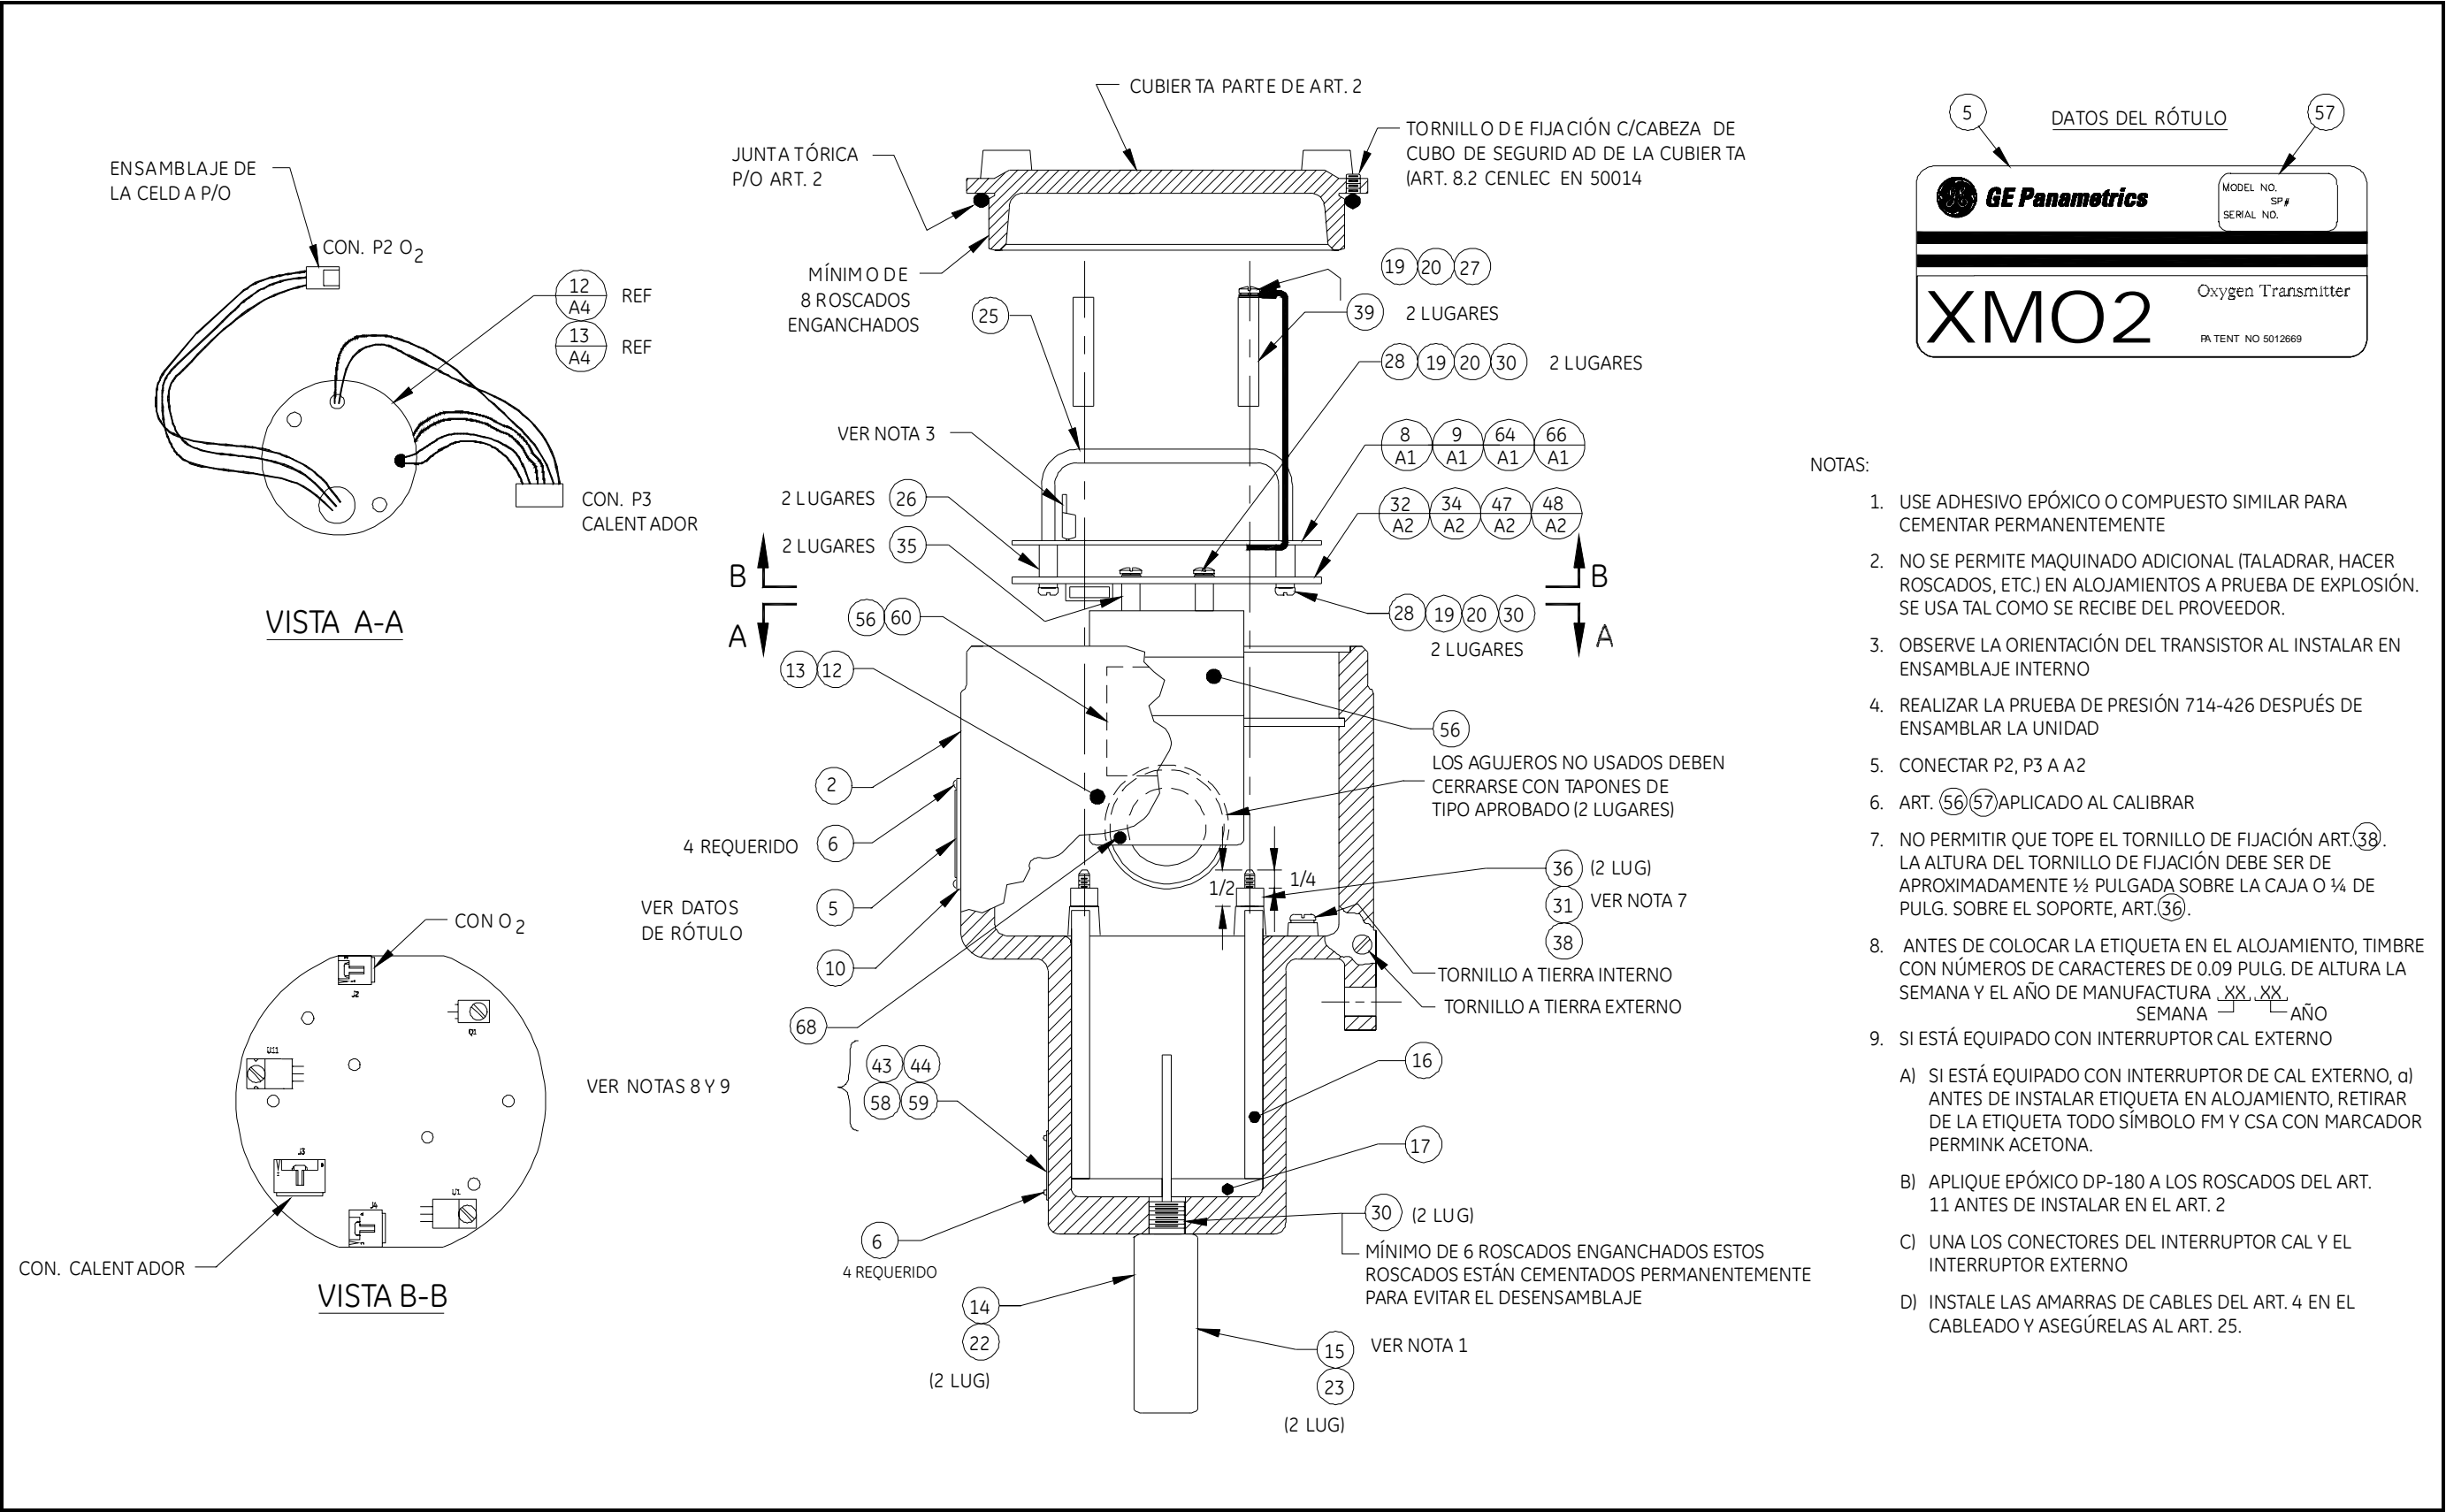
Esquema de ensamble (Esq. 705-677H)
